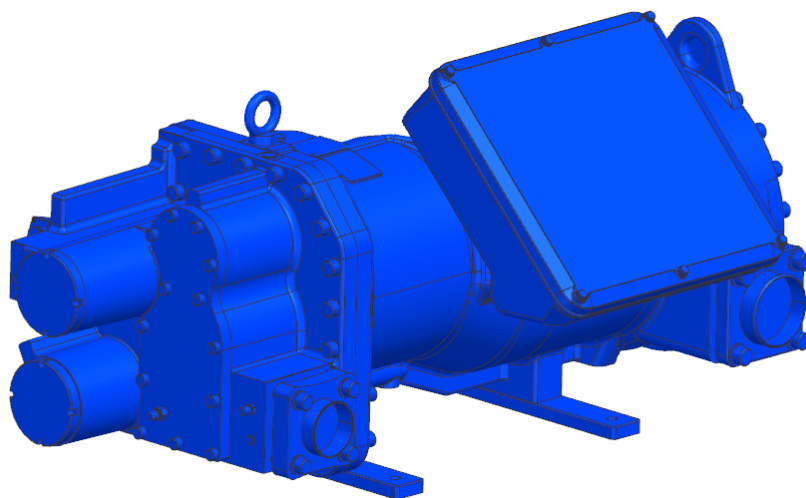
Compressore Frascold FVR-H-160-400ALU
